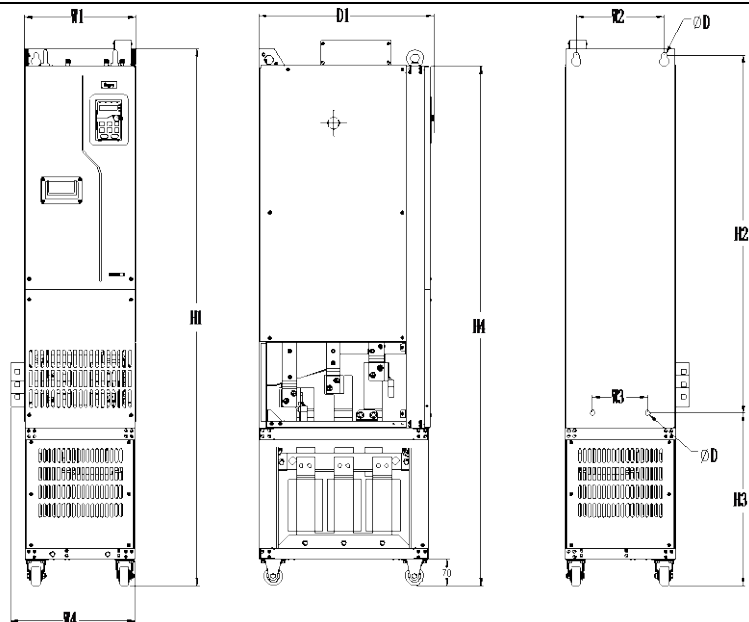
Чертеж для напольного монтажа моделей ПЧ 380В 220–500кВт с выходными реакторами
